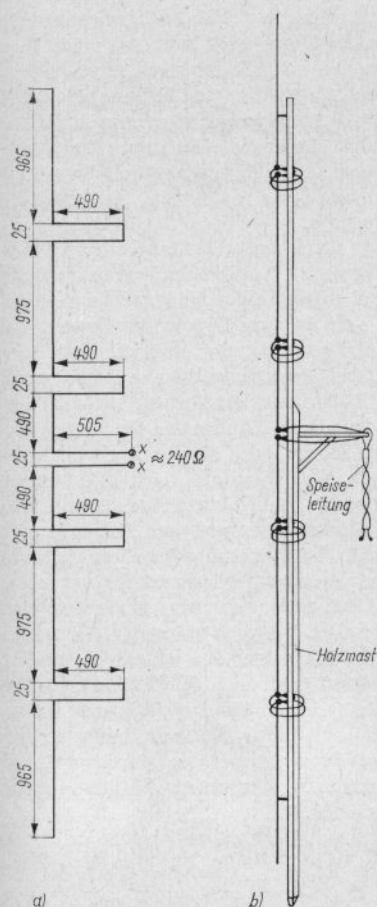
Vertikale Dipolzeile mit 5 Elementen für das 2-m-Band; a – Bemessungsschema, b – Aufbauvorschlag
